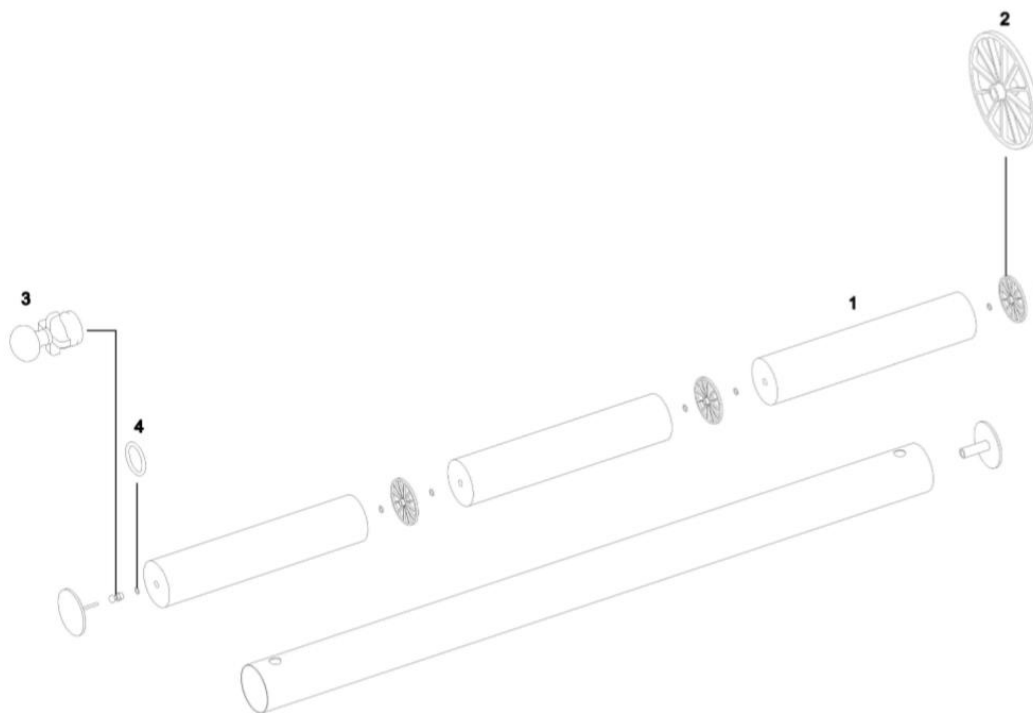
Схема установки мембранных элементов в напорный корпус
